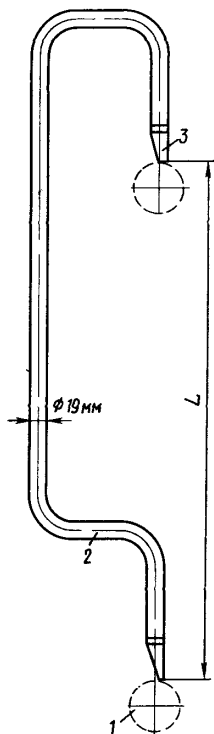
Приспособление для проверки межцентрового расстояния цапф зубчатых колес привода сушильной части:
